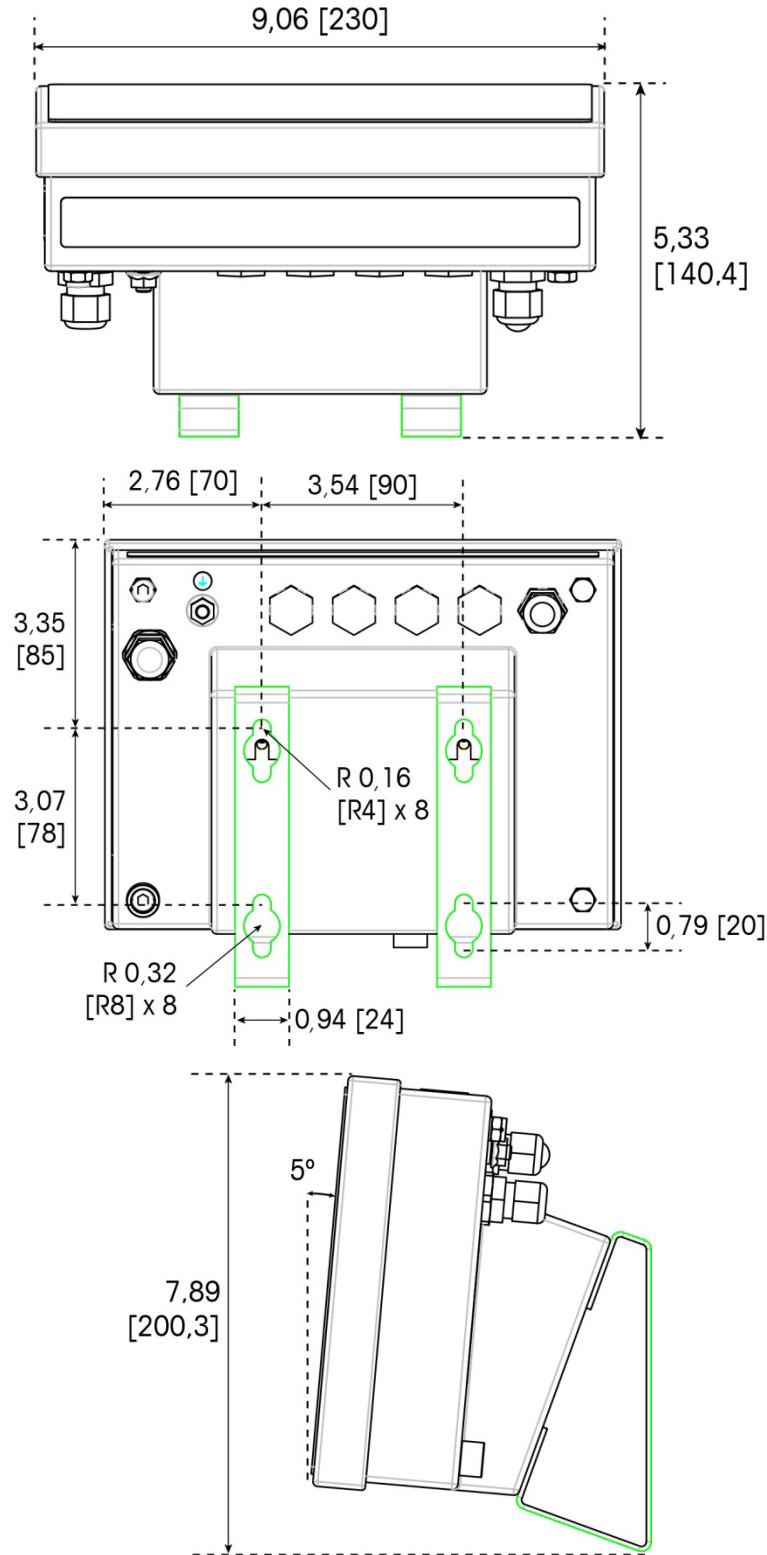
Dimensioni IND245x, con staffa fissa per montaggio a muro
